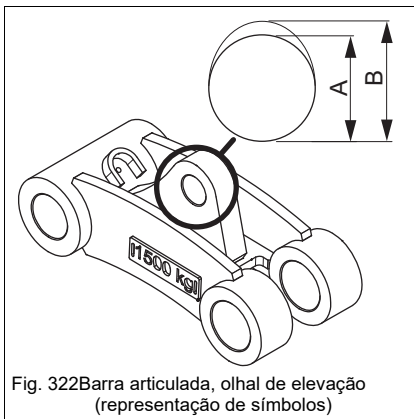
Barra articulada, olhal de elevação (representação de símbolos)
